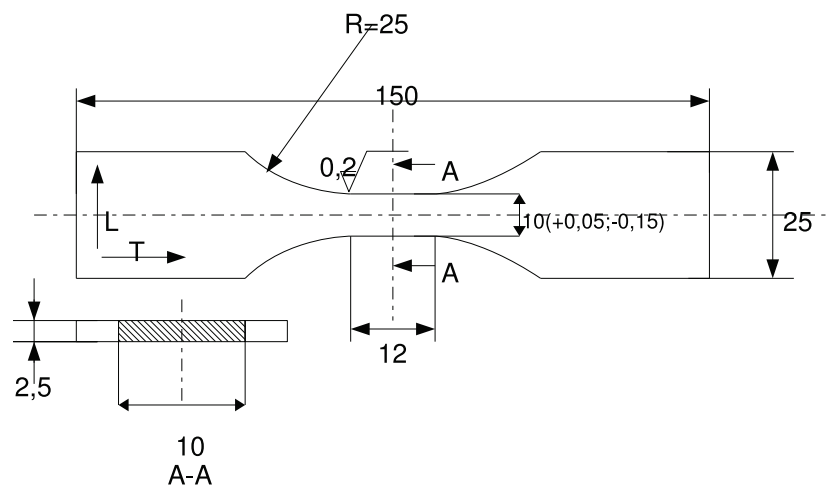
Géométrie de l'éprouvette VDEH
